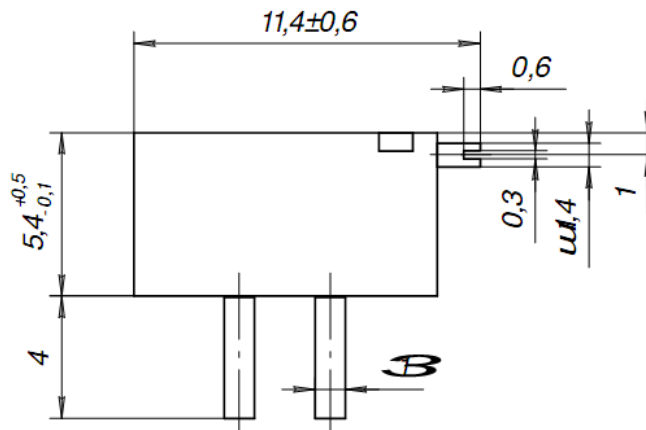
Габаритні розміри резистора СП5-2ВБ
